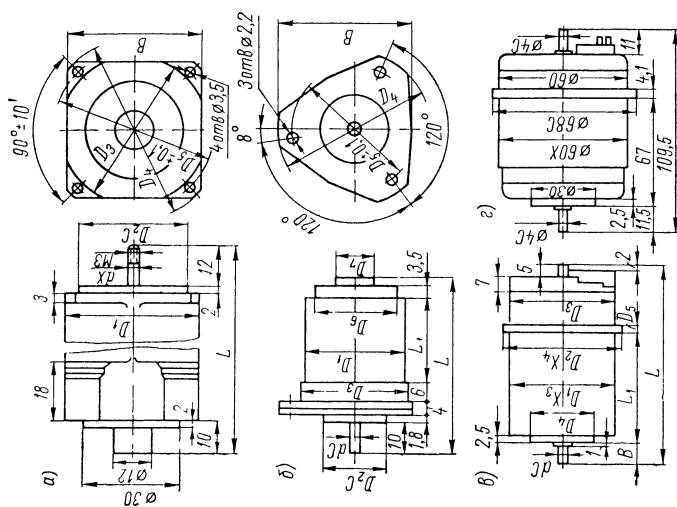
Обозначения размеров асинхронных электродвигателей с полым ротором: а — типа ЭМ; б — типа ДИД; в — типа АДП; г — типа ИБ.762 050
